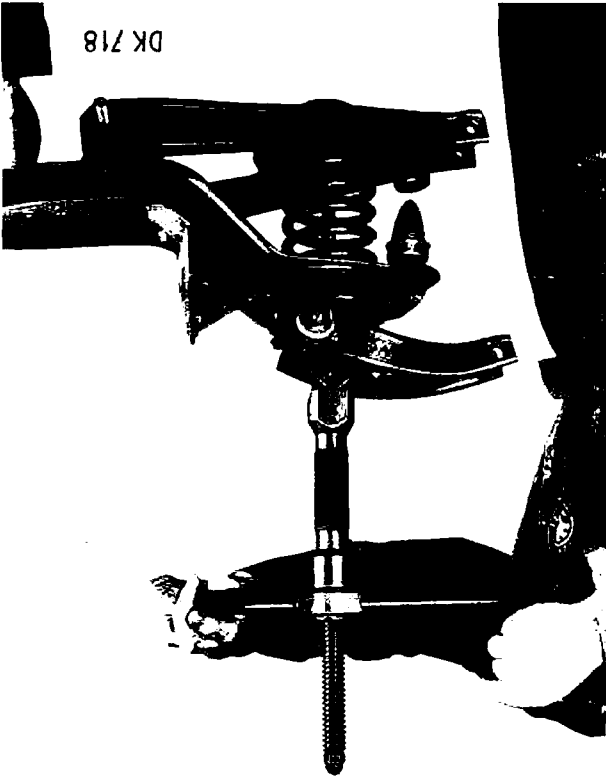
/4 Zusammendrücken der Vorderachs-schraubenfeder mit der Montagevorrichtung MP 6-106
